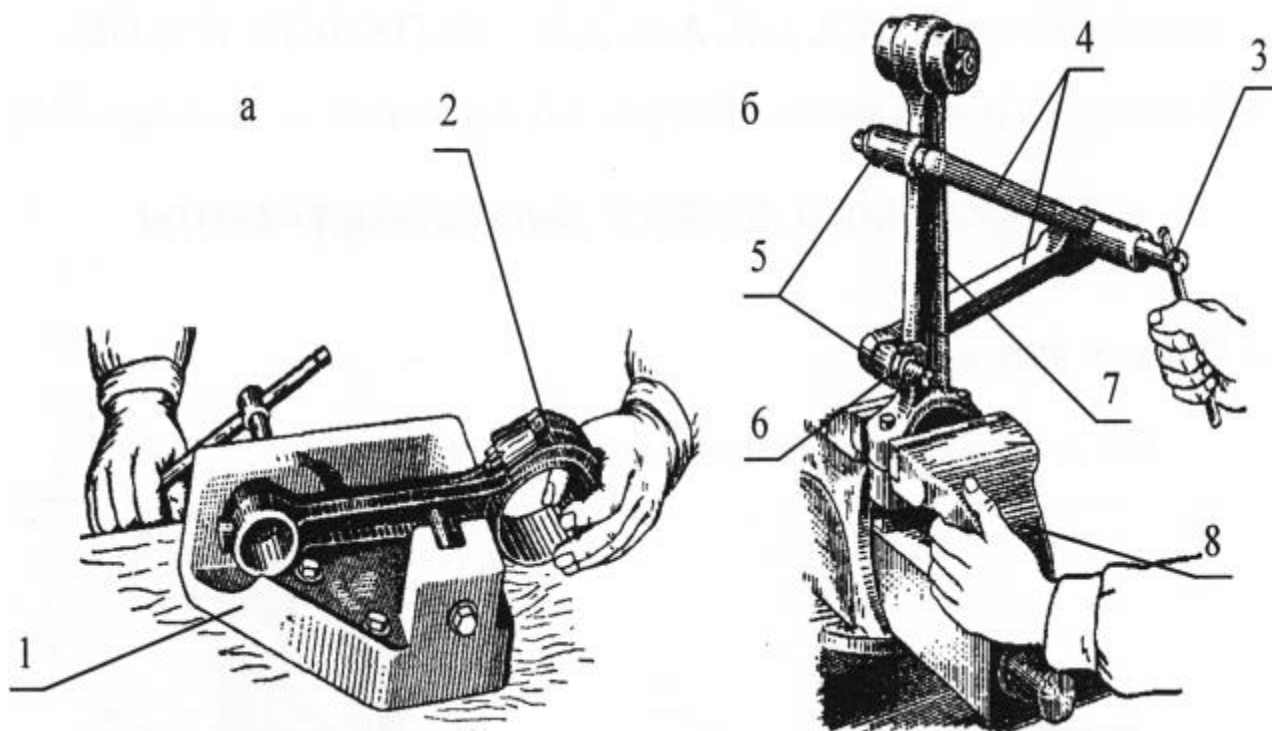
Правка шатунов: а - изогнутых; б - скрученных; 1 - приспособление для выправления изгиба; 2, 7 - шатун; 3 - разводной винт; 4 - рычаги; 5 - упорные накладки; 6 - зажимная гайка; 8 - тиски.
